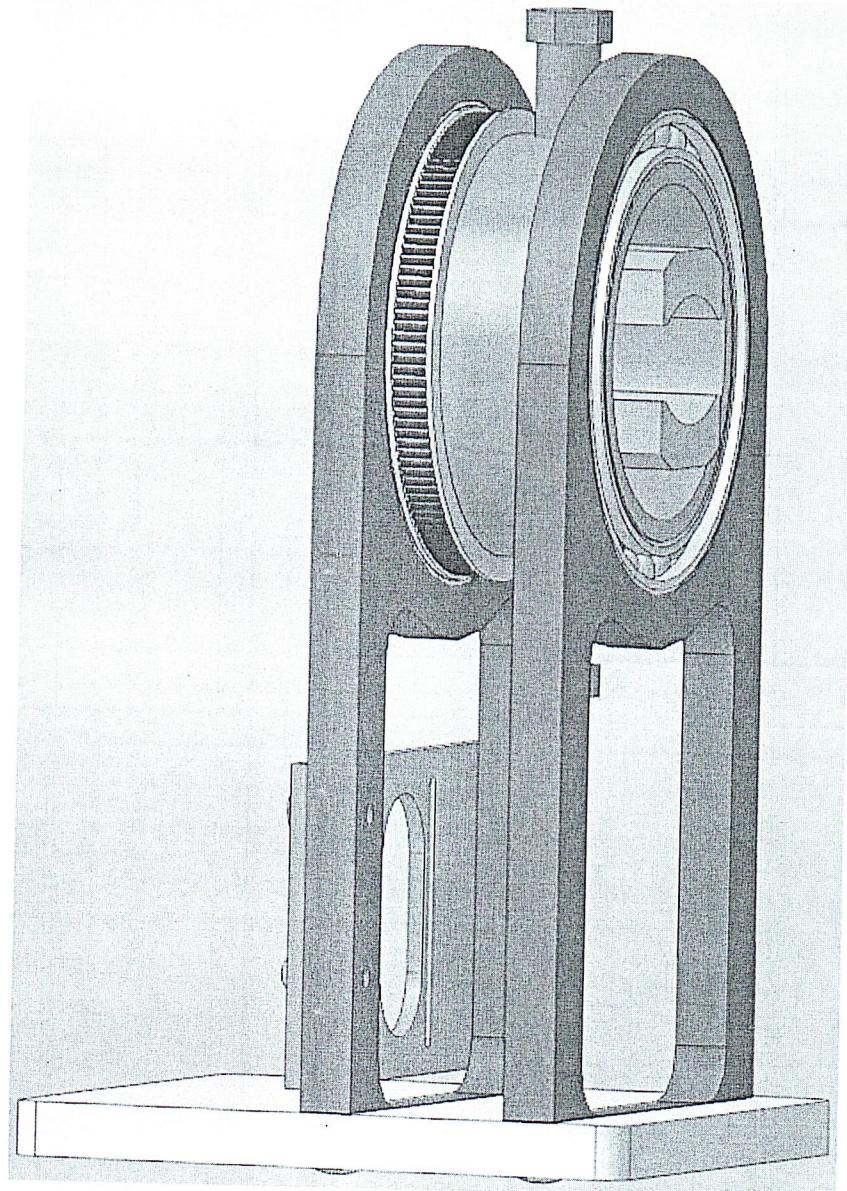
3D сборка сварочного вращателя «закрытого»
